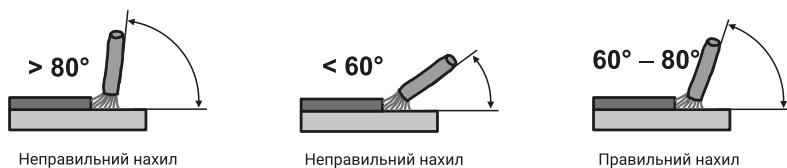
Варіанти кута розташування електрода із покриттям до деталі під час ручного дугового зварювання («ММА»).
